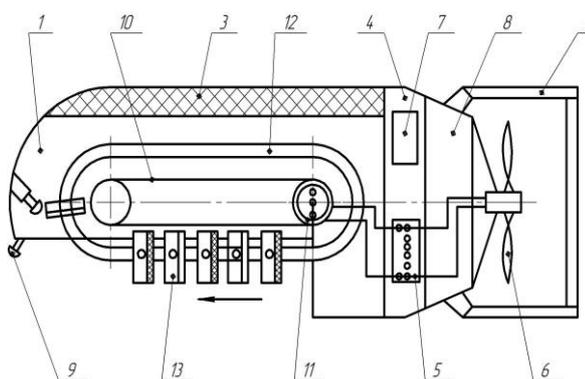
Глубоководное планирующее грунтозаборное устройство
